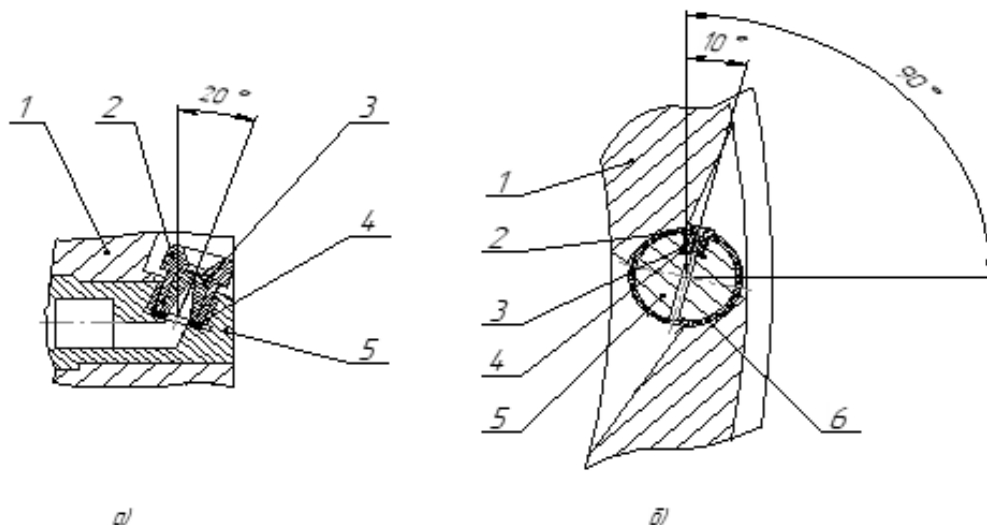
Вузол розвантаження барабана сепаратора: а) до модернізації; б) після модернізації; 1 - основа барабану; 2 - обойма сопла; 3 - сопло; 4 - ущільнення; 5 - корпус сопла; 6 - ущільнююча втулка
